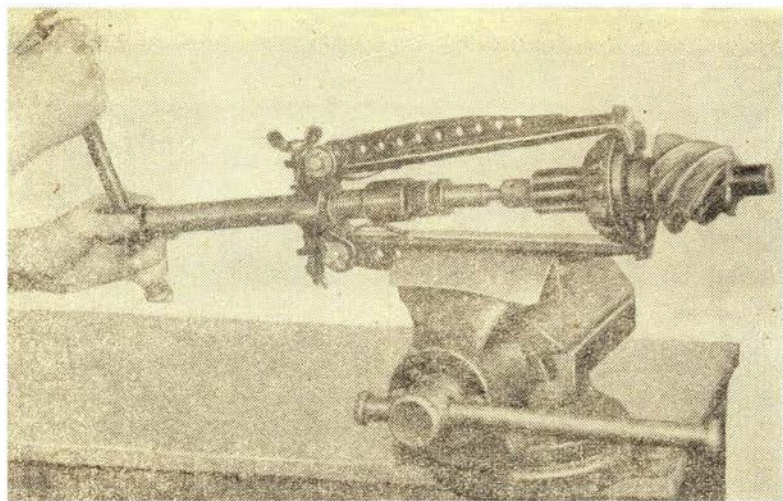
Снятие внутреннего кольца заднего роликового подшипника
